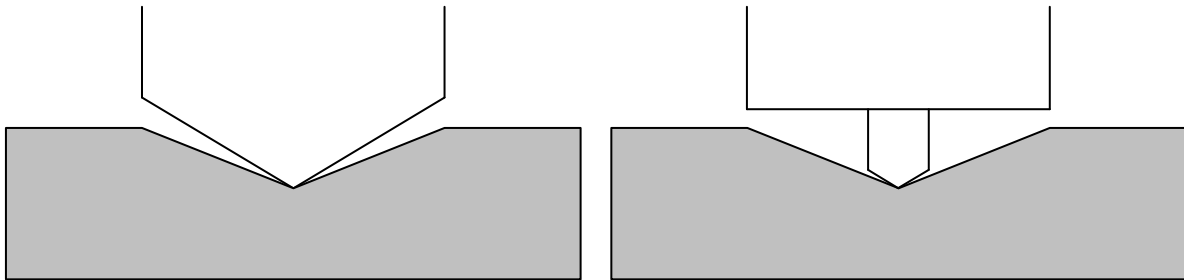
Maße bei Bohrer (links) und verstellbarem Spindelwerkzeug (rechts)
